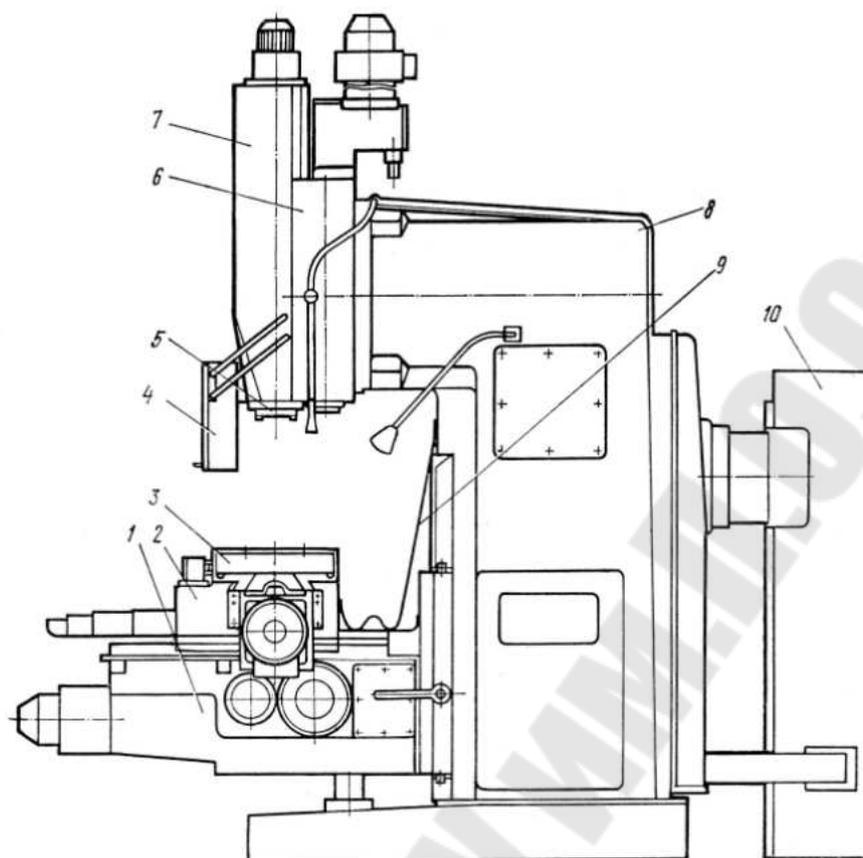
Профильная проекция общего вида вертикально-фрезерного станка 6Р13Ф3-37:
